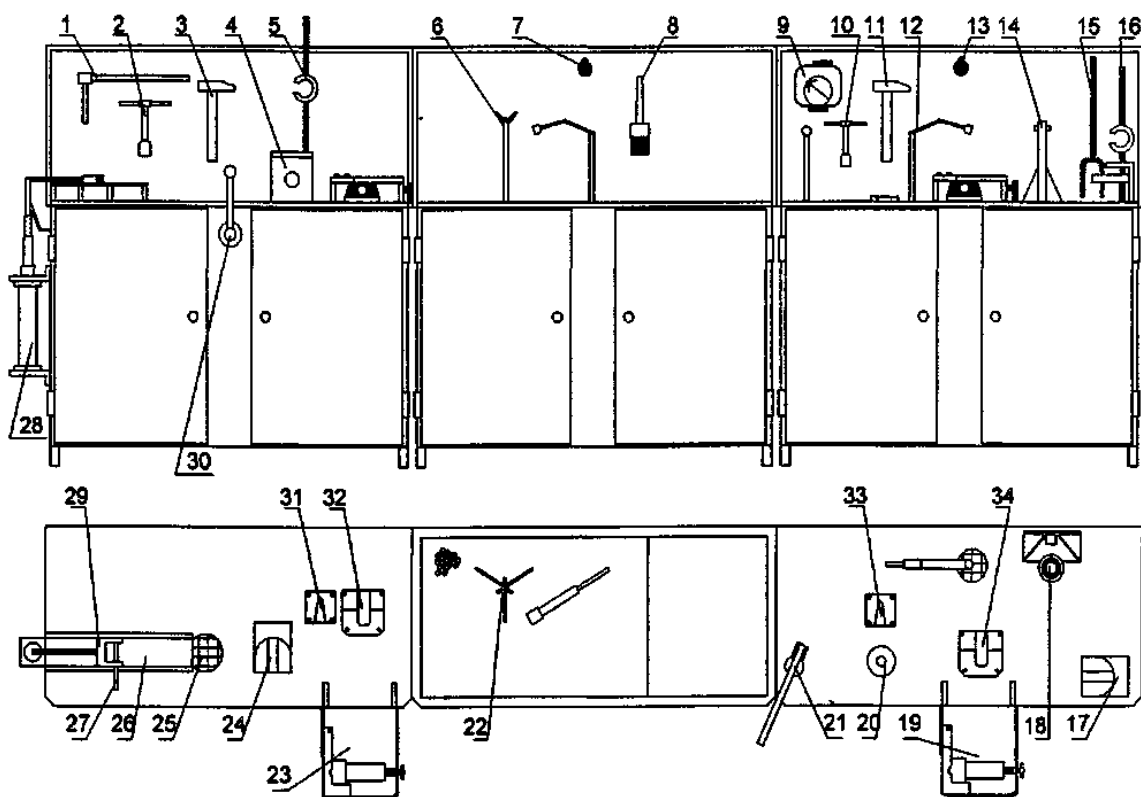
Стенд «ЭНГА» для разборки, ремонта и сборки гидравлических гасителей колебаний
